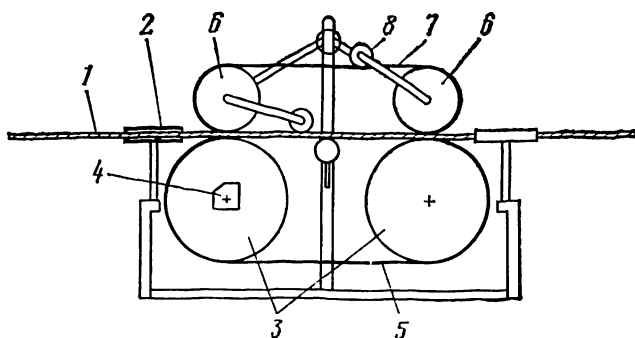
Измеритель длины со сдвоенными мерительными колесами. 1 — изделие; 2 — калибры; 3 — мерительные колеса; 4 — счетчик; 5 — приводной ремень; 6 — прижимные ролики; 7 — прижимной ремень; 8 — натяжные ролики.
